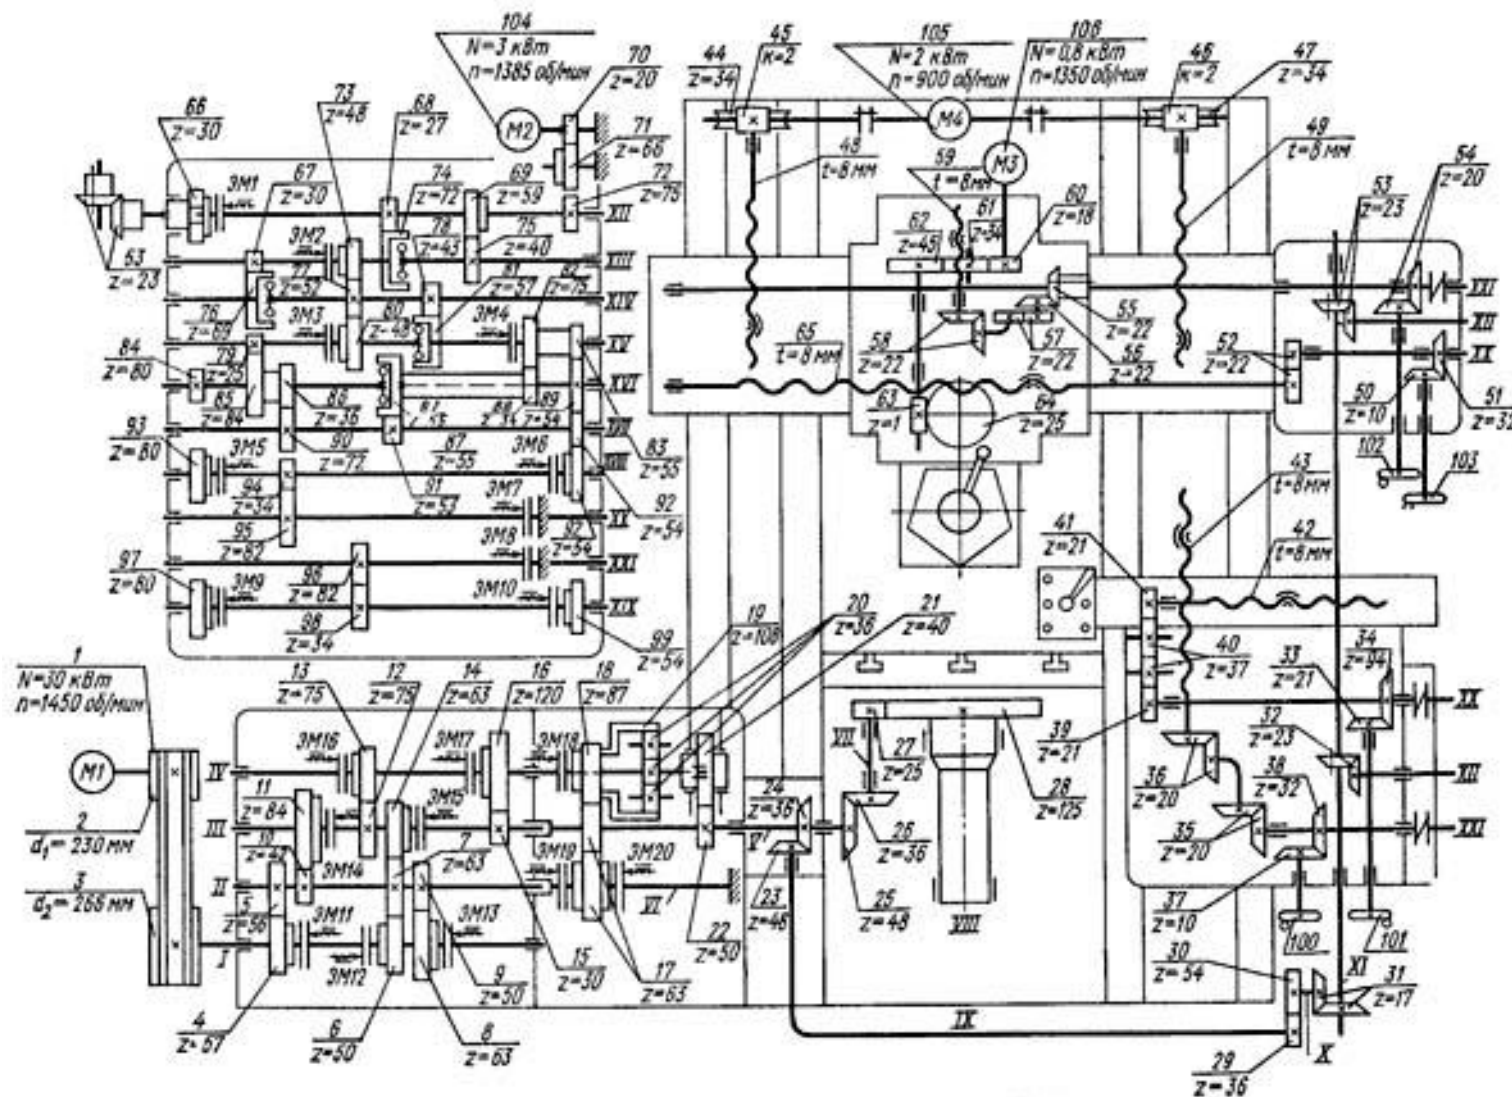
Кінематична схема токарно-карусельного верстата 1516
